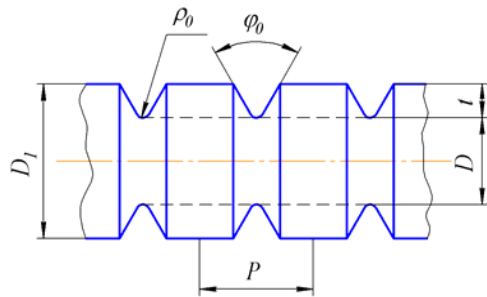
Цилиндрическая деталь с V-образными надрезами
